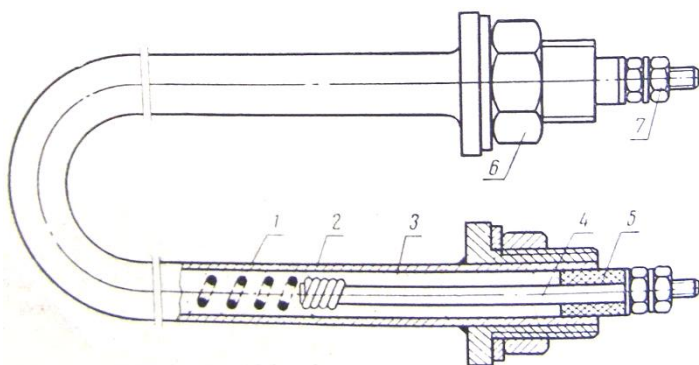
Трубчатый электронагреватель (ТЭН) герметического исполнения: 1 – нихромовая спираль; 2 – трубка; 3 – наполнитель; 4 – выводная шпилька; 5 – герметизирующая уплотнительная втулка; 6 – гайка для крепления; 7 – выводы.
